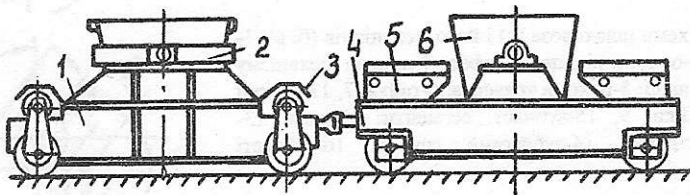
Комплекс візків для транспортування металів і шлаків: 1-металовозний приводний візок; 2-кран для металу; 3-привод механізму переміщення; 4-шлаковозний візок; 5-шлаковня; 6-кран для шлаку
